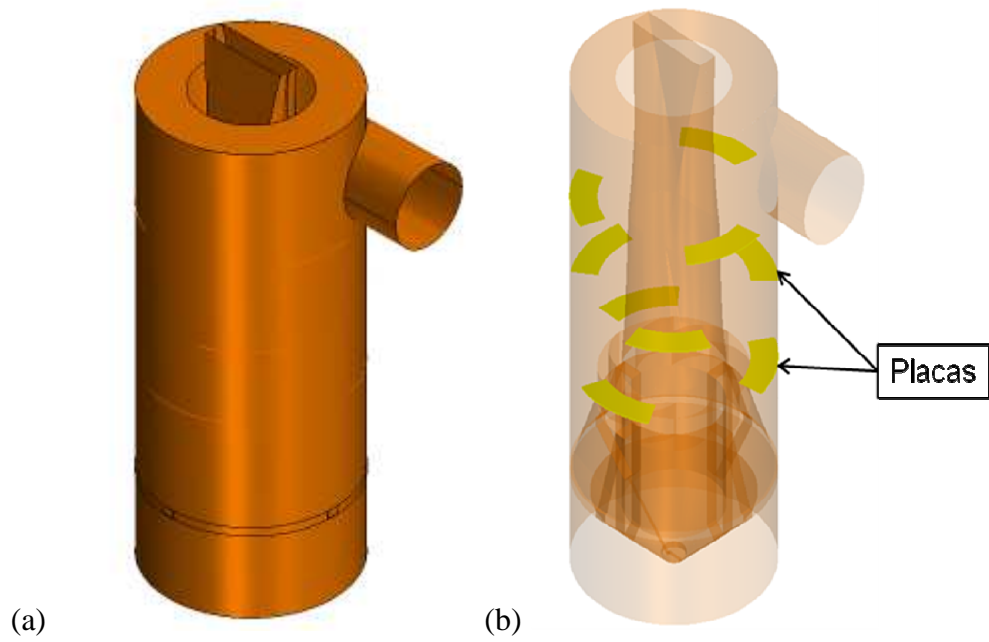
Primeira proposta - (a) Vista Externa e (b) Posição das Placas
